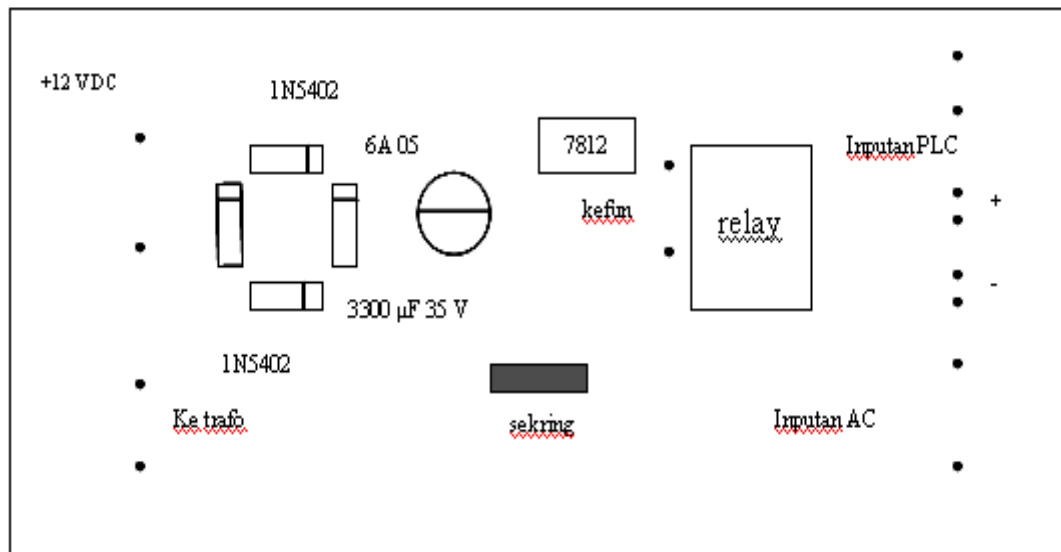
Layout PCB jalur penyearah, relay dan jalur AC
